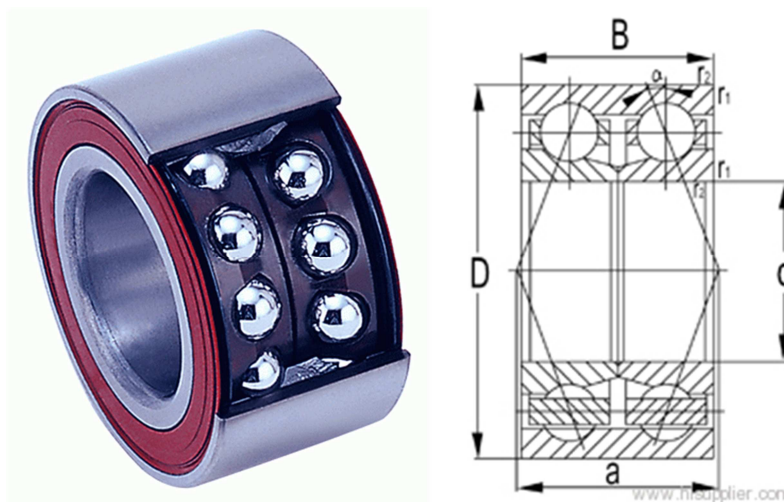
2 Rodamiento de bolas de contacto angular.
